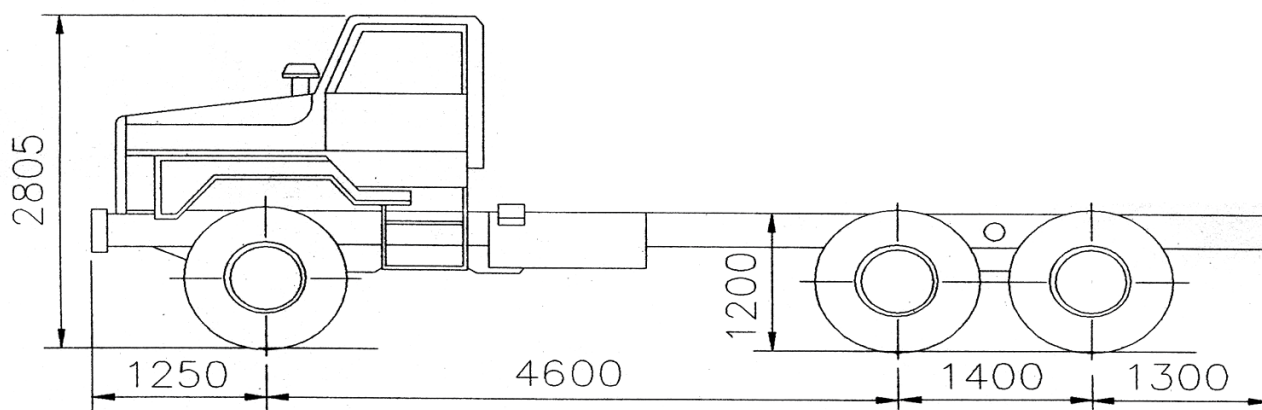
Основные габаритные размеры автомобиля Урал-4320
